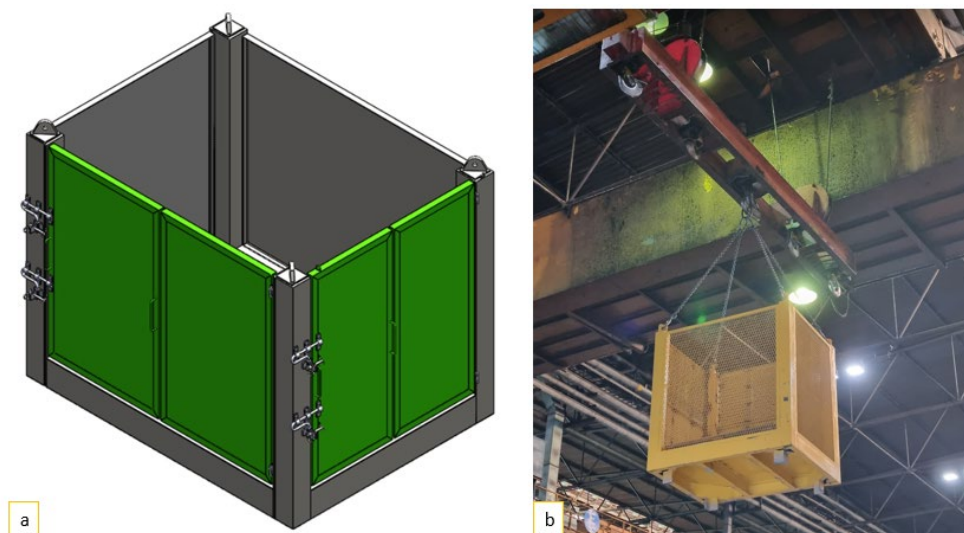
Jaula porta pallet: a) render, b) prueba de izaje con puente grúa.
